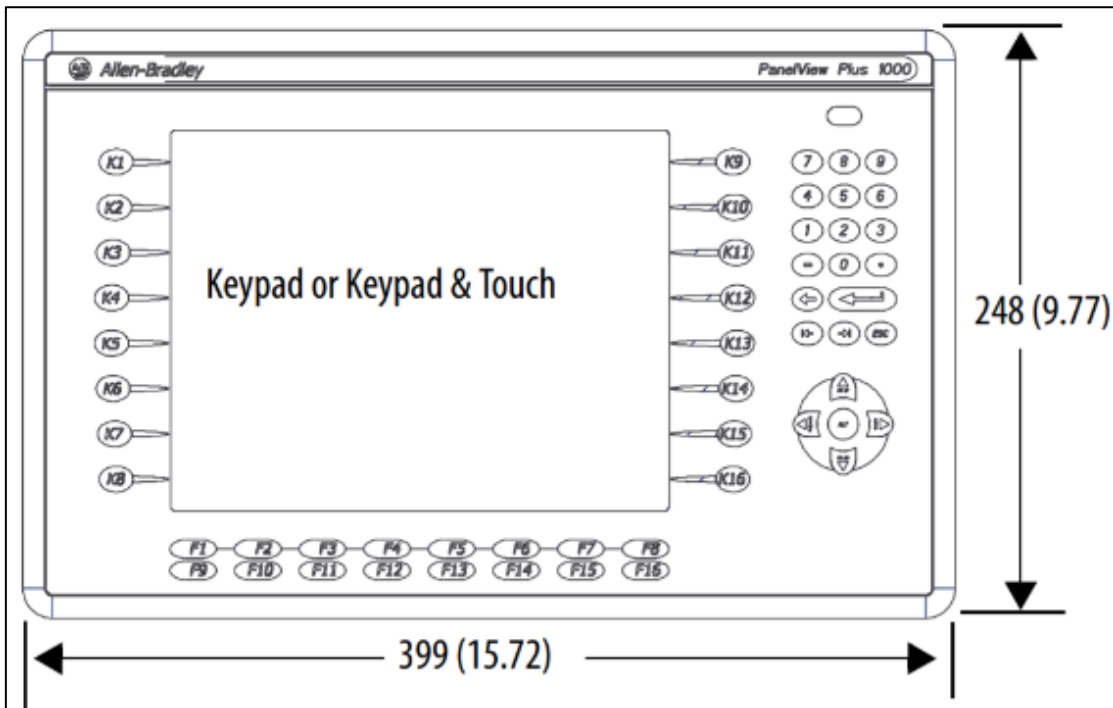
DIMENSIONES DE FRENTE DEL PANELVIEW
